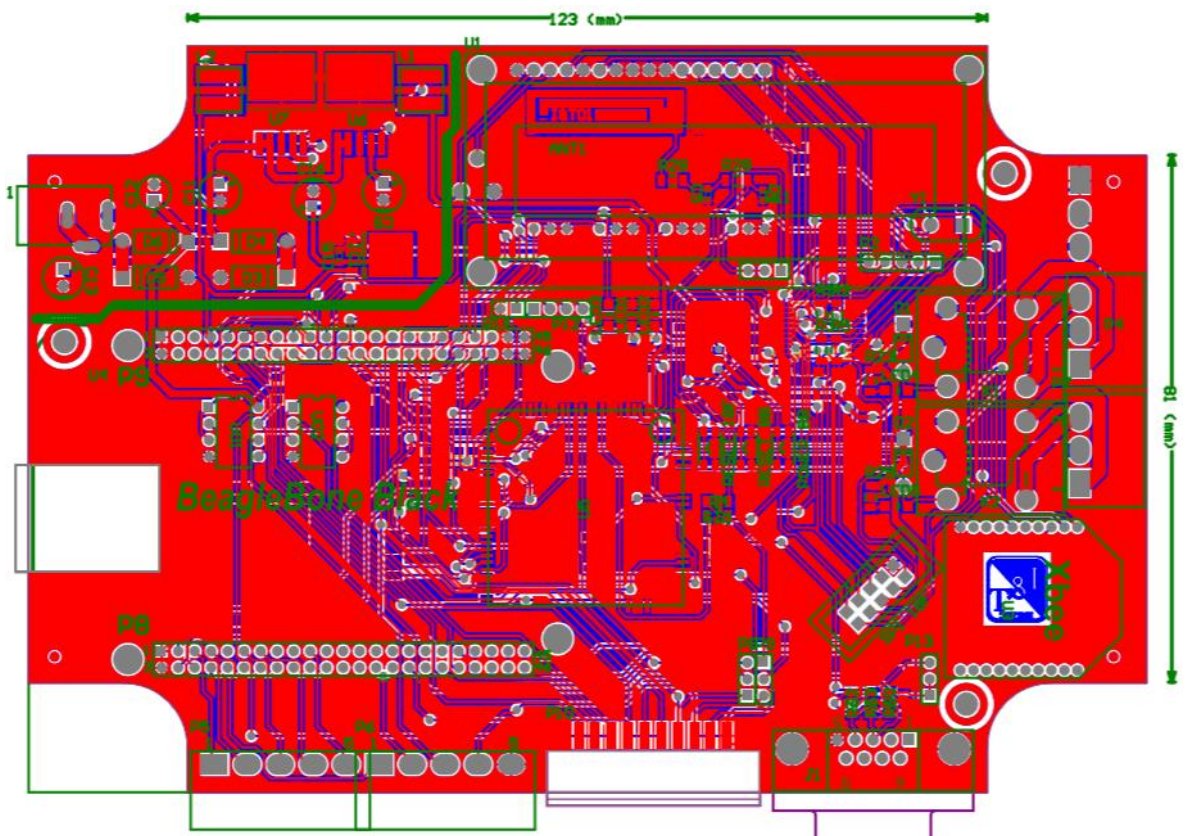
5: Esquemático del circuito impreso de la placa de expansión.
